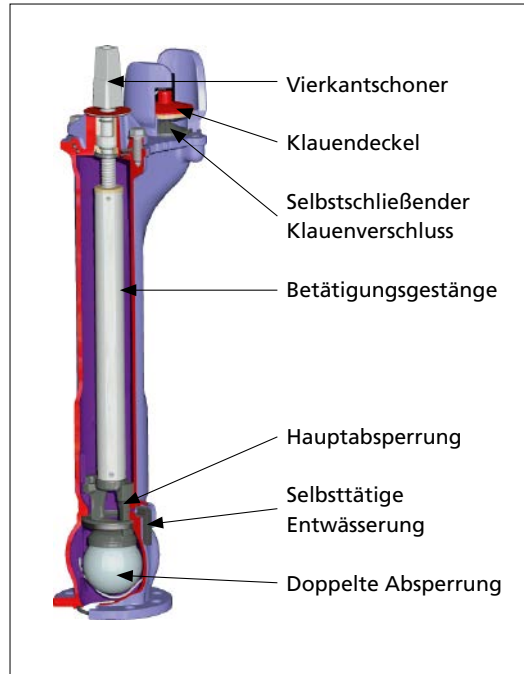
Unterflurhydrant DN 80 – doppelte Absperrung, Öffnungsrichtung entgegen der Strömungsrichtung – Beschichtung mit Epoxidharzpulver
